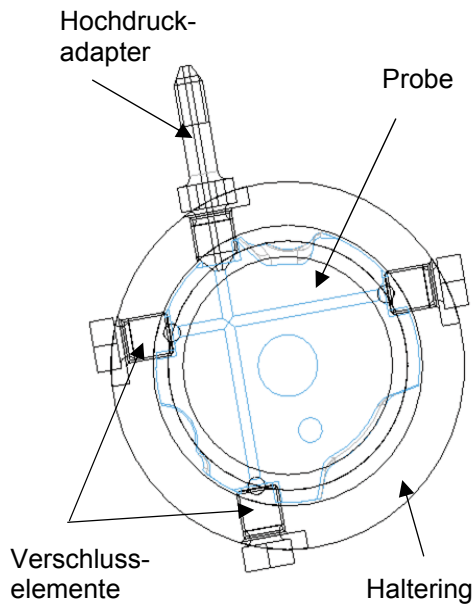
Aufspannung der Bauteilprobe für die Einstufenversuche
